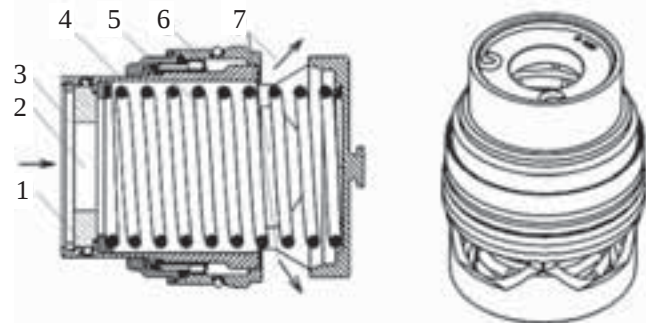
Разрез и общий вид картриджа: 1 – шайба; 2 – входное отверстие; 3 – стопорное кольцо; 4 – гильза; 5 – пружина; 6 – затвор клапана; 7 – регулирующие отверстия
